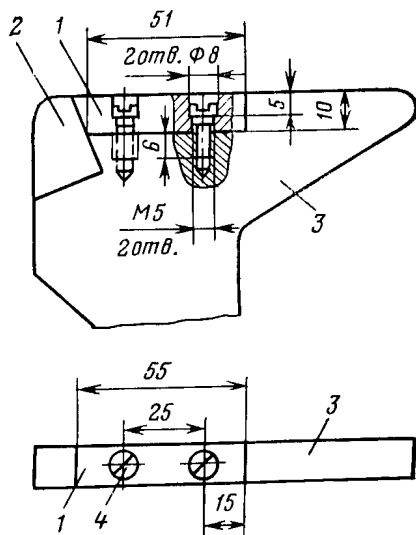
Установка дополнительной металлокерамической пластины КМК Б-21 (ГОСТ 13333—83)
